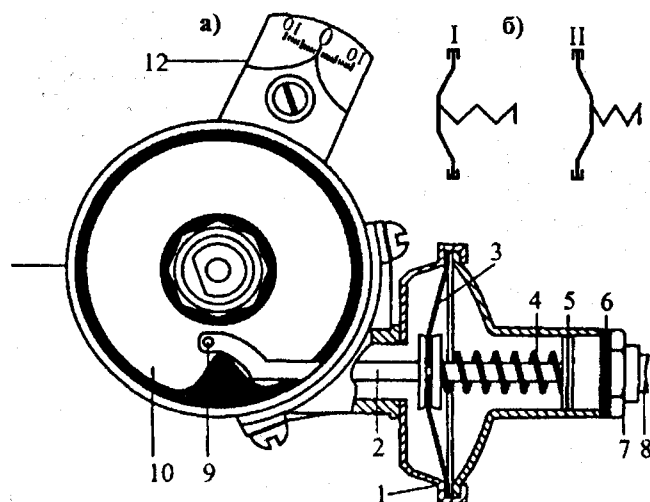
Устройство вакуумного регулятора: а) 1 – корпус регулятора; 2 – тяга; 3 – диафрагма; 4 – пружина; 5 – регулировочная прокладка; 6 – уплотнительная прокладка; 7 – штуцер; 8 – трубка; 9 – штифт; 10 – подвижная пластина; 11 – корпус прерывателя; 12 – октан-корректор; б) – положение диафрагмы: I – при большей нагрузке; II – при меньшей нагрузке
